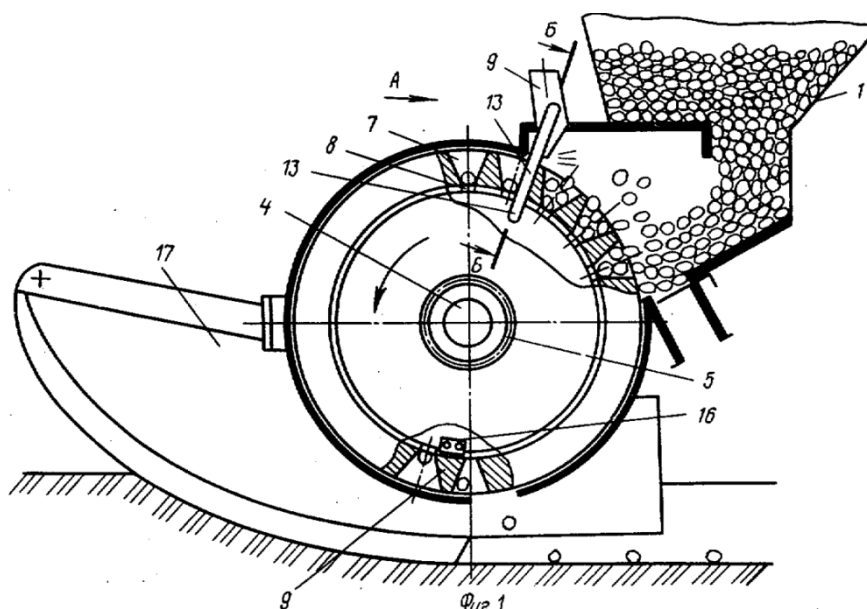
Пневматический высевальный аппарат, вид с боку:
